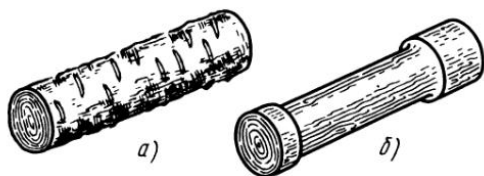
Заготовка кряжа для естественной сушки с поперечными прорезами коры (а) и со снятием коры в средней части (б)
